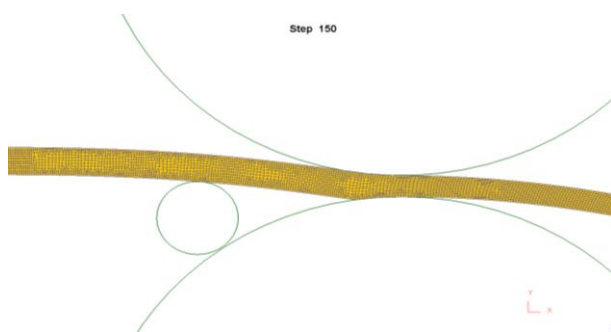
Расположение ролика, задающего угол наклона заготовки
